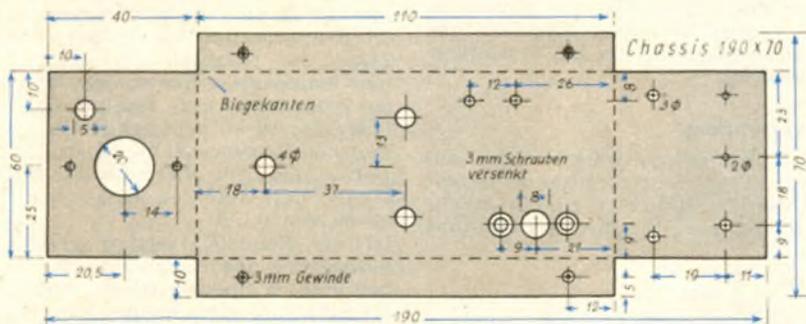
Maßskizze für das Chassis des HF-Verstärkers
